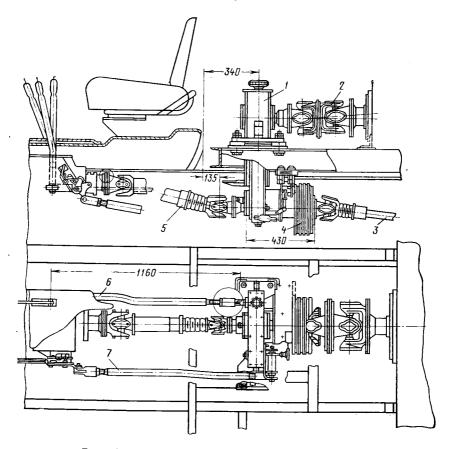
Трансмиссия агрегата Азинмаш-35А: 1 — коробка отбора мощности; 2 — карданный вал насоса; 3 — карданный вал заднего моста; 4 — тормозной барабан; 5 — карданный промежуточный вал; 6 — тяга скоростей; 7 — тяга тормоза
